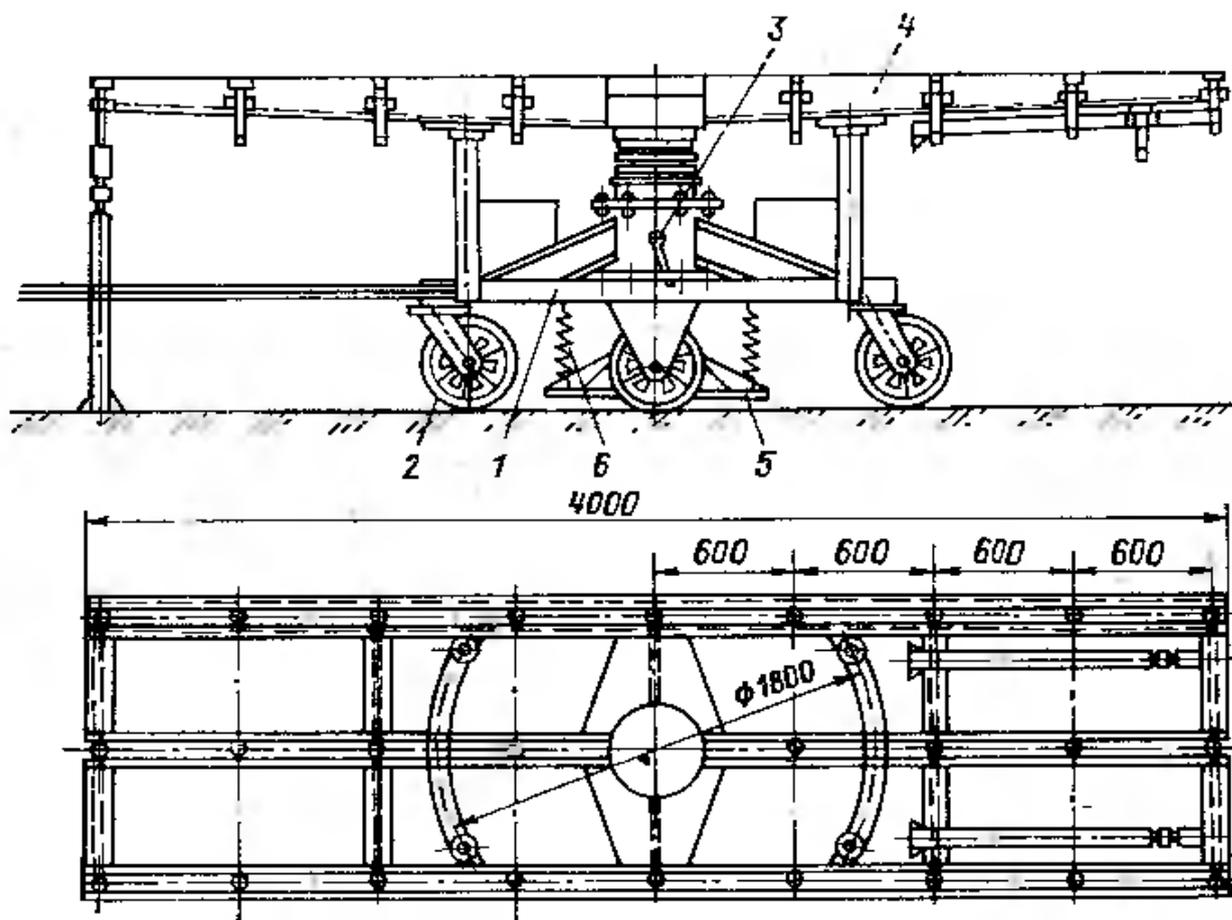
Агрегат для замены днищевой обшивки корпуса.
